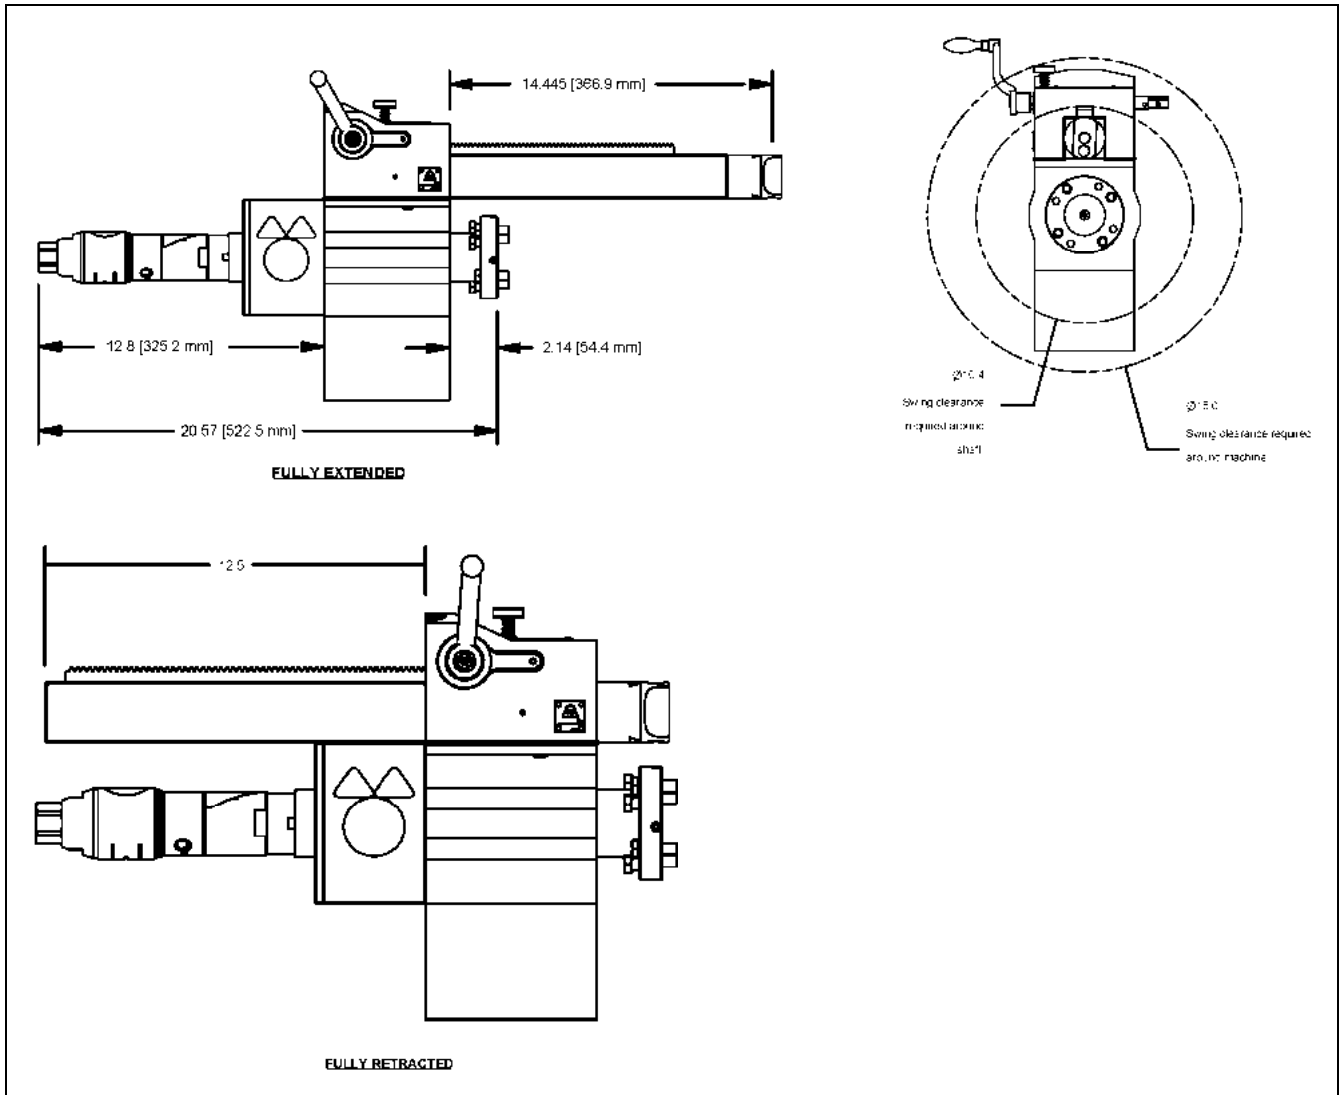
DIMENSIONS DE DEGAGEMENT DU TOUR PORTATIF PNEUMATIQUE (POUCES/MM)
